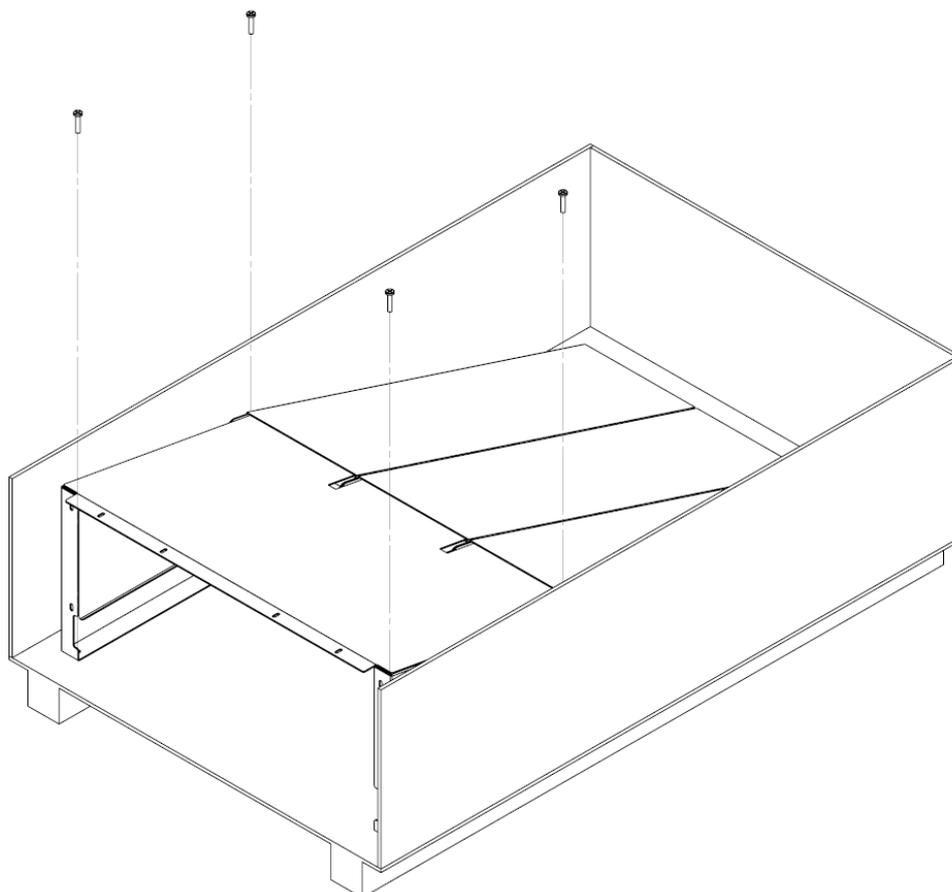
Remoção dos parafusos de fixação da Rampa da Caixa de Embalagem
